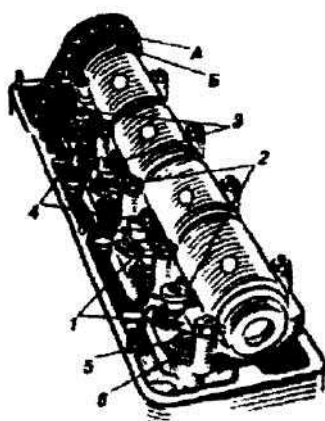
Проверка и регулировка тепловых зазоров клапанов механизма газораспределения двигателя ВАЗ-2101: А и Б - метки, при совмещении которых поршень в 4-м цилиндре достигает в.м.т. на такте сжатия; 1-4 очередность регулировки клапанов; 5 - регулировочный болт; 6 – контргайка.
